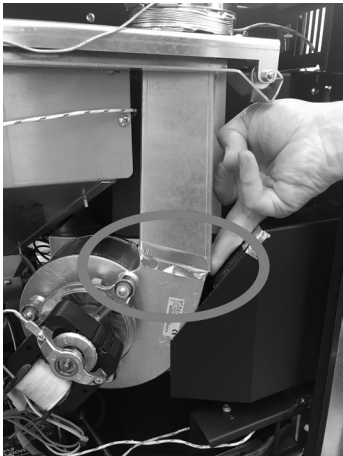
Sceller avec du ruban adhésif en aluminium
